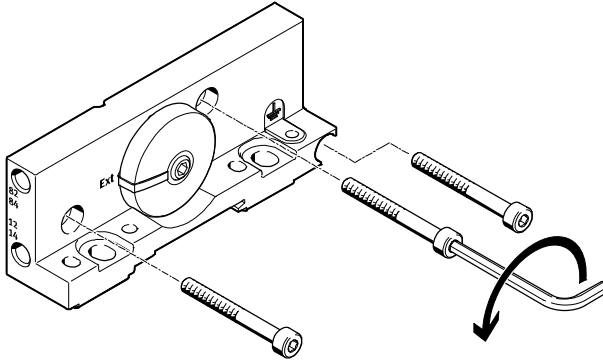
Schrauben der Zuganker an der rechten Endplatte lösen
